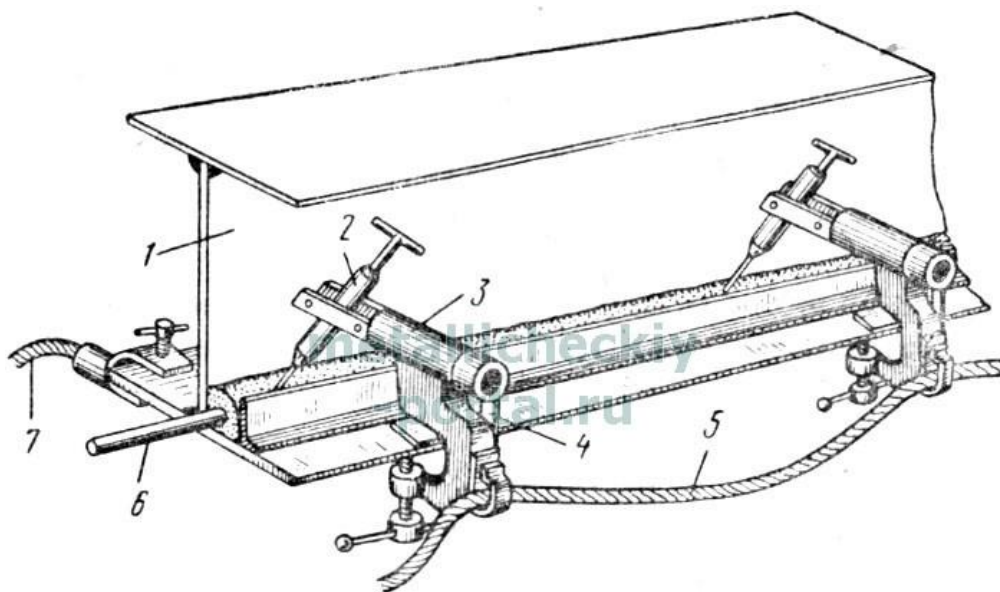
Сварка лежачим электродом под слоем флюса:
